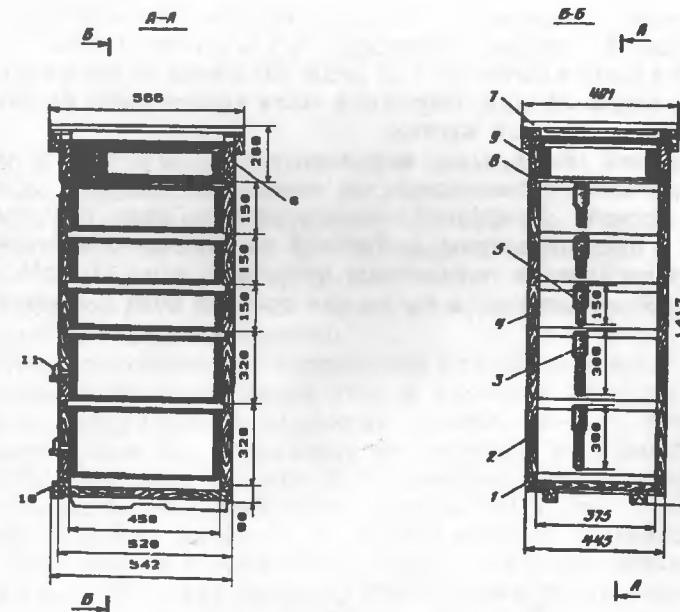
Улей двухкорпусный с магазинами (т.к. 3.808-2).
